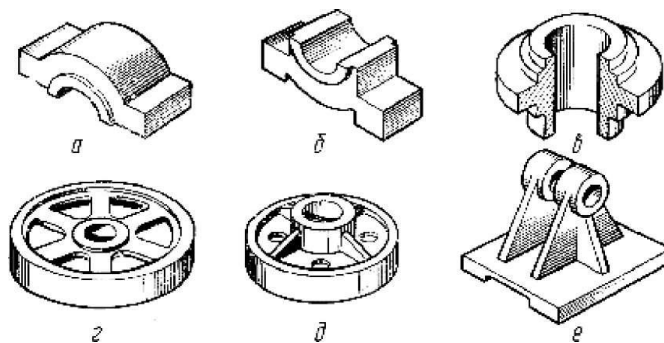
Примеры несложных отливок (II группа сложности): *а* - крышка подшипника; *б* - корпус подшипника; *в* - ступица; *г* - зубчатое колесо; *д* - ролик;
